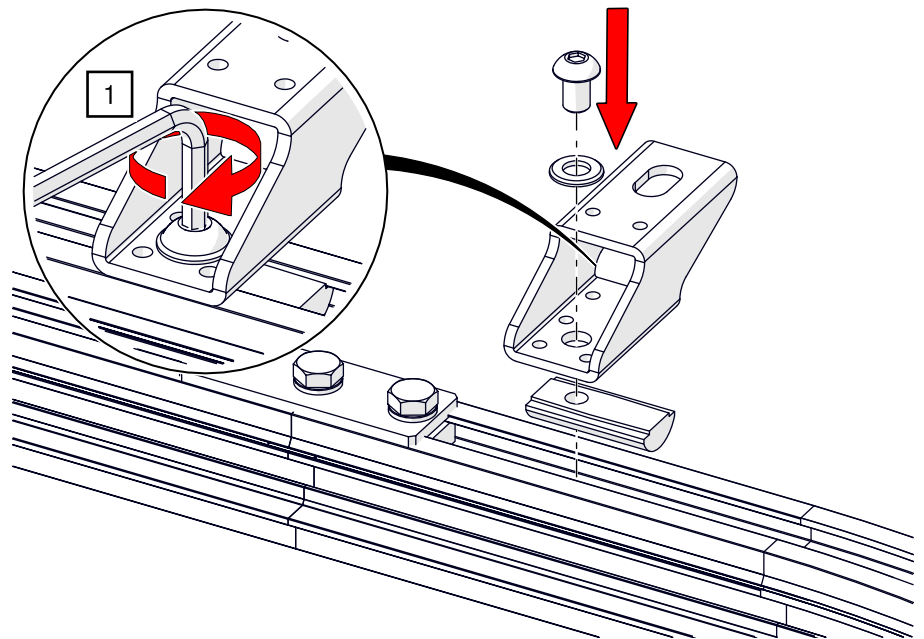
Deckenmontage – Abhängung an dem Schienenprofil montieren
